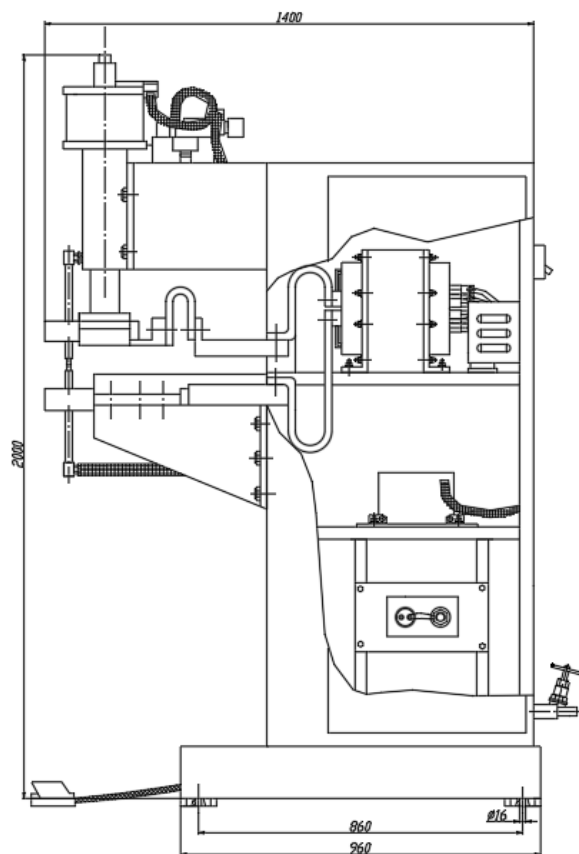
Машина для контактної точкової зварювання МТ-1215 (вид збоку)
